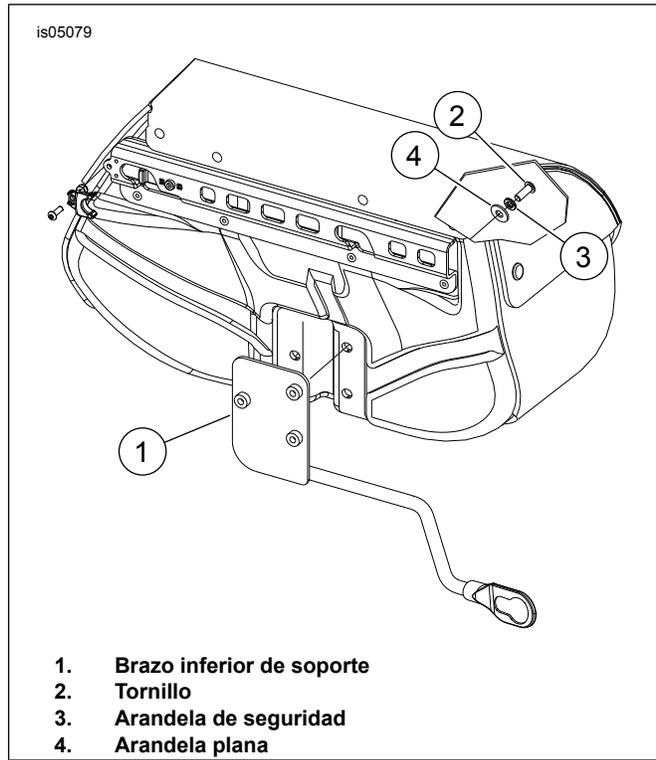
Conjunto de la pieza de soporte del soporte izquierda inferior
